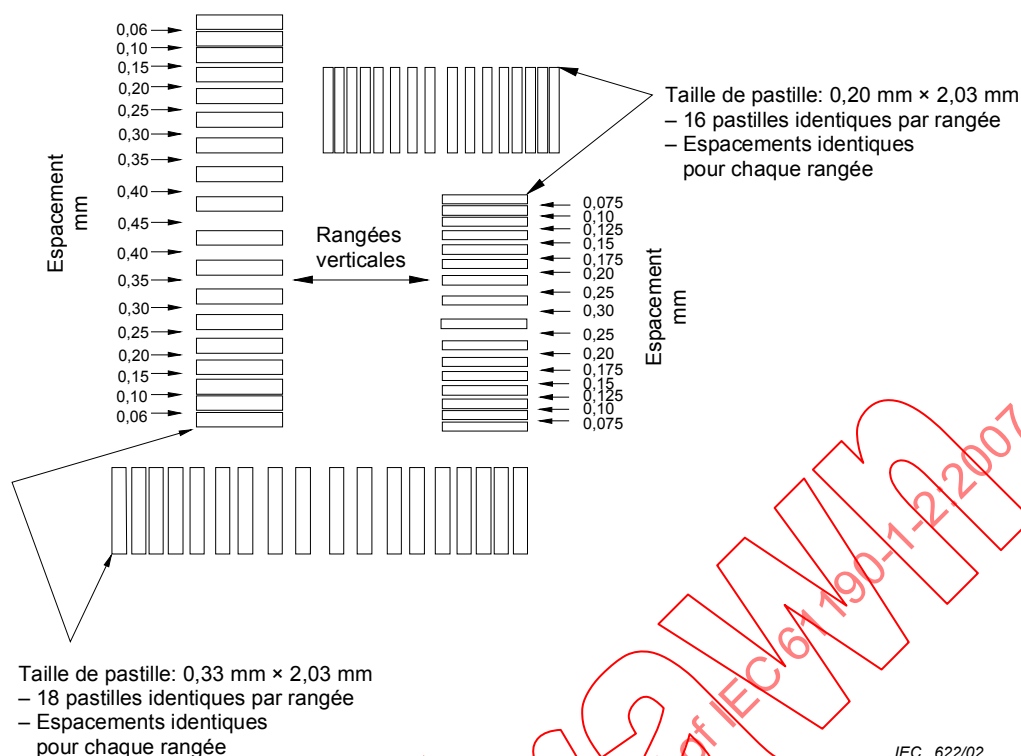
Epaisseur du pochoir de l'essai d'affaissement, 0,10 mm
